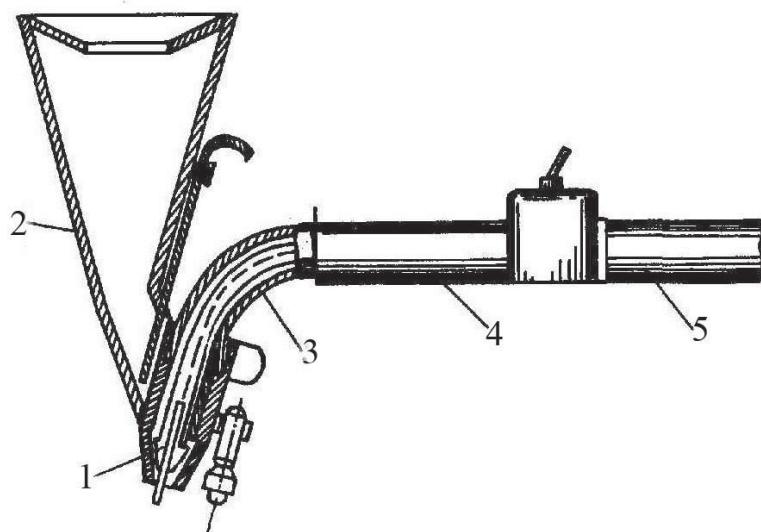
Держатель полуавтомата для сварки под флюсом:
